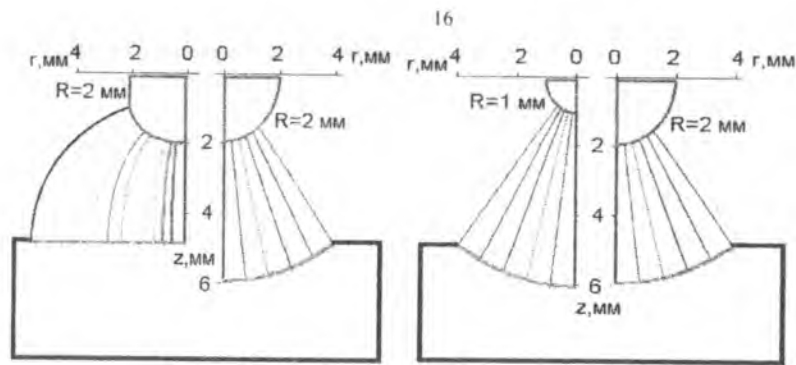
Силовые линии сварочной дуги: а) для плоской и вогнутой сварочной ванны б) при разных радиусах электрода.
